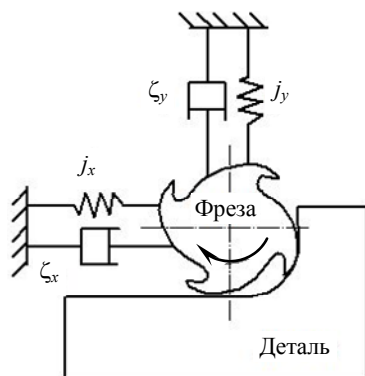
Жесткость фрезы на порядок меньше жесткости детали и станка
